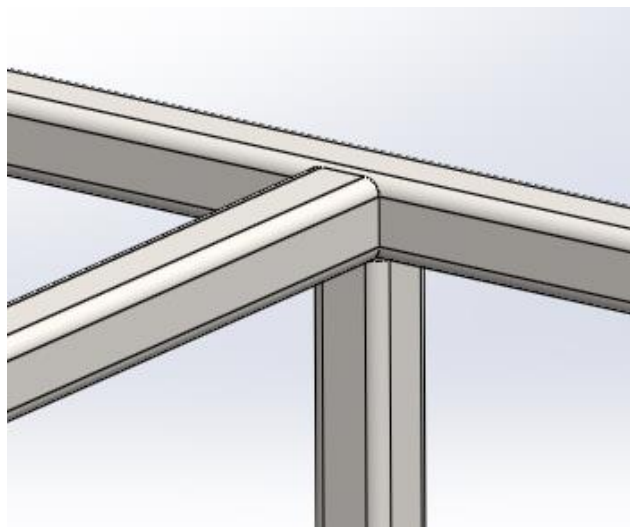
Detalle juntas soldadas (Refuerzos)
